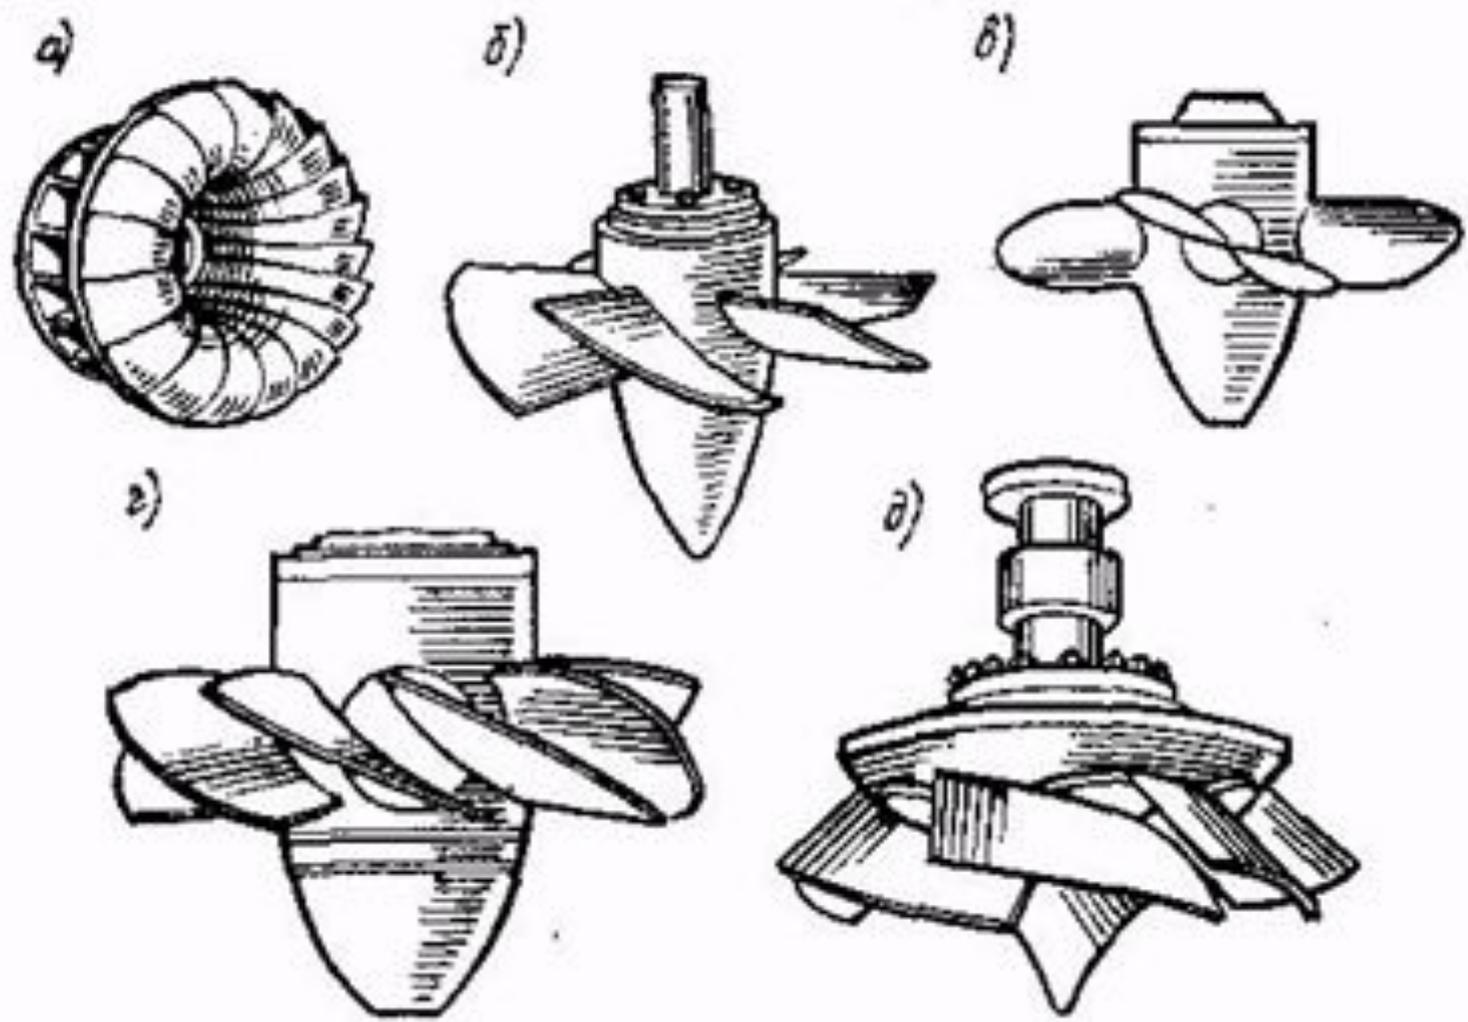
Общий вид рабочих колес реактивных турбин:
